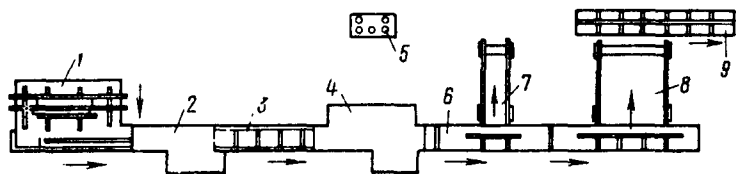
Автоматическая линия ДВ505 обработки брусков дверной коробки:
